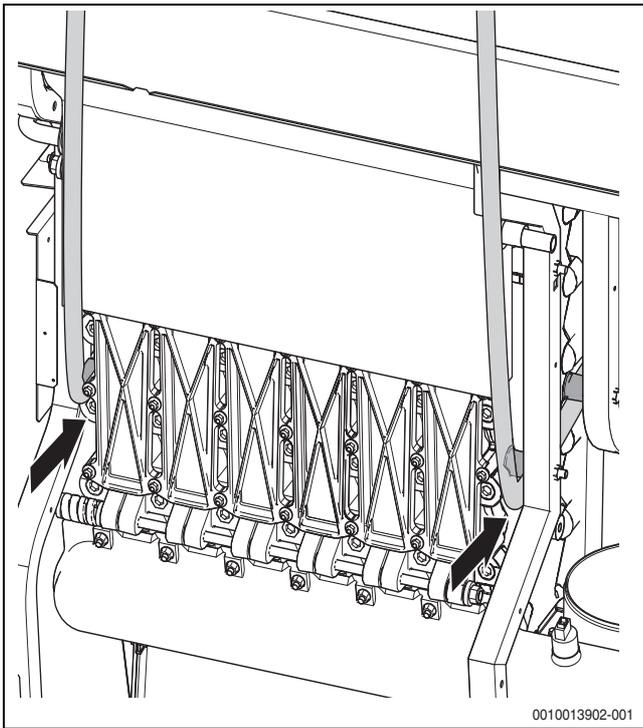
Disposizione dell'imbracatura della gru sul telaio
